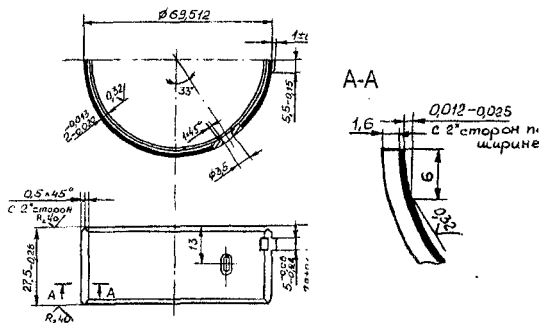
Чертеж вкладыша шатунного подшипника двигателя ЗИЛ-130
